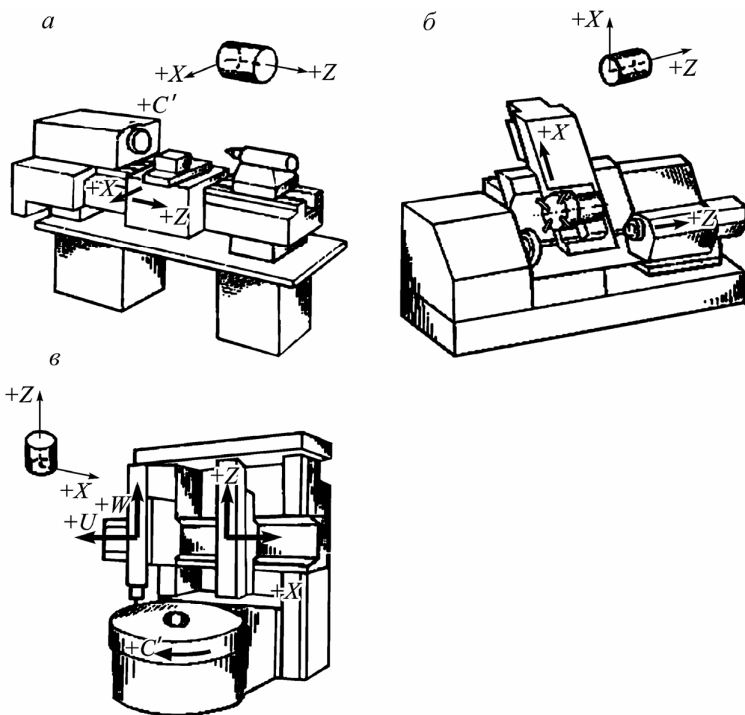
Движения в токарных (а, б) и токарно-карусельных (в) станках с ПУ
